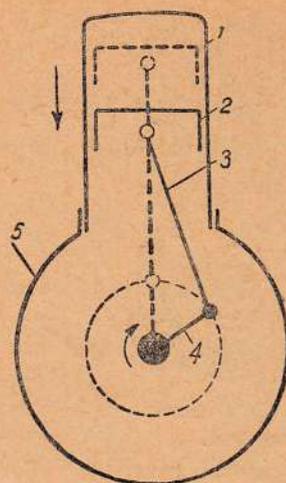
Схема двигателя: 1 — цилиндр, 2 — поршень, 3 — шатун, 4 — коленчатый вал, 5 — картер.
